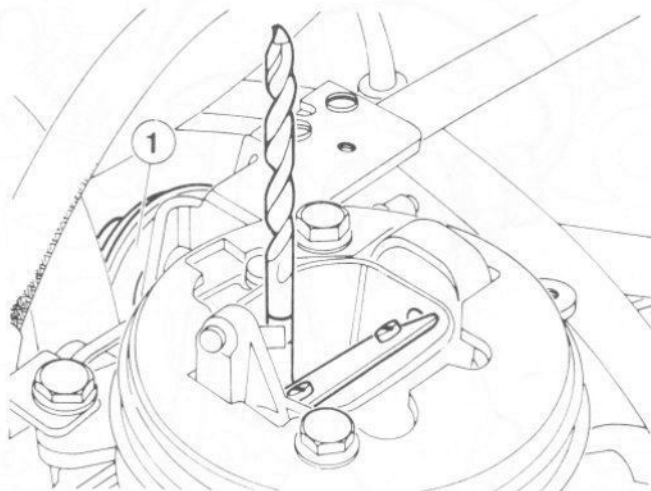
Réglage de l'OVAD - carburateur Weber 36 TLC (Sec 8)
